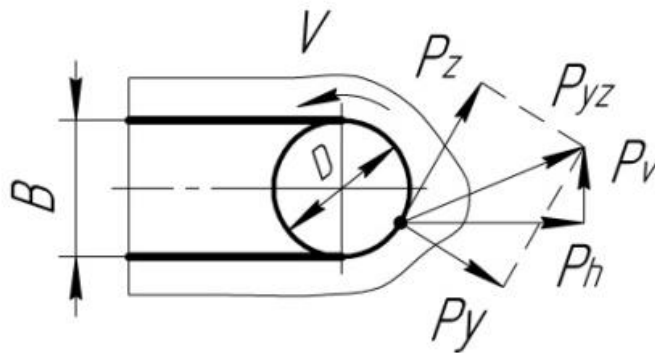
Схема дії сил різання при фрезеруванні паза шириною 8 мм
